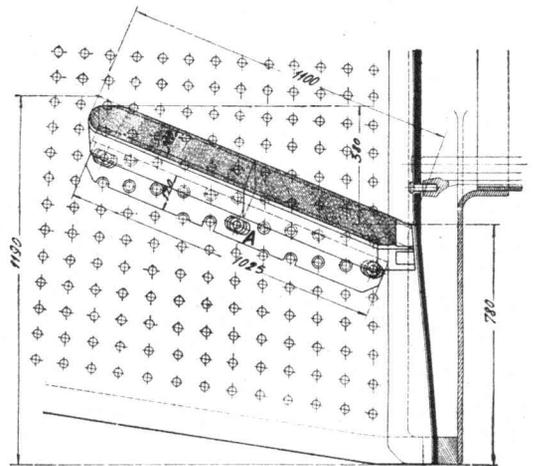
Feuergewölbtträger, Befestigung mittels Stehbolzen. (Distanzschrauben.)
